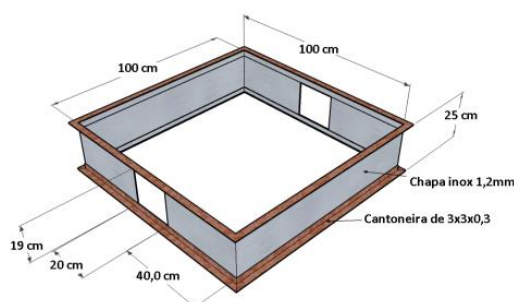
Módulo 1 ou base metálica para a construção da câmara inferior da fornalha.
